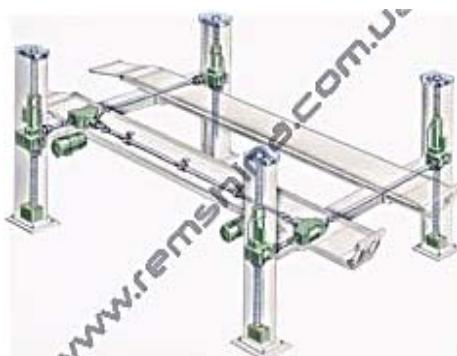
Четырехстоечный подъемник с червячными и коническими редукторами и карданной передачей в приводе
